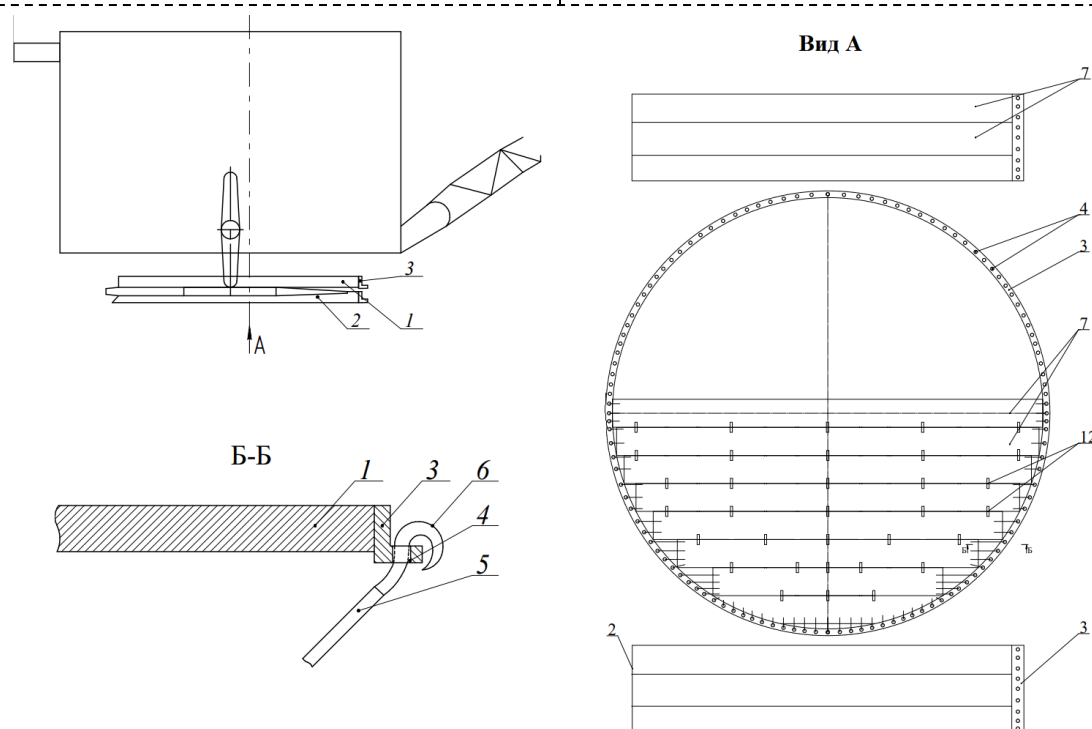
Фронтальный вид экскаватора и вид А при использовании варианта с применением транспортерных лент и их расположение: 1 – опорная база экскаватора; 2 – лыжи; 3 – балка крепления; 4 – отверстия в балке; 5 – трос крепления; 6 – крюк; 7 – отрезок конвейерной ленты; 12 – элемент крепления
